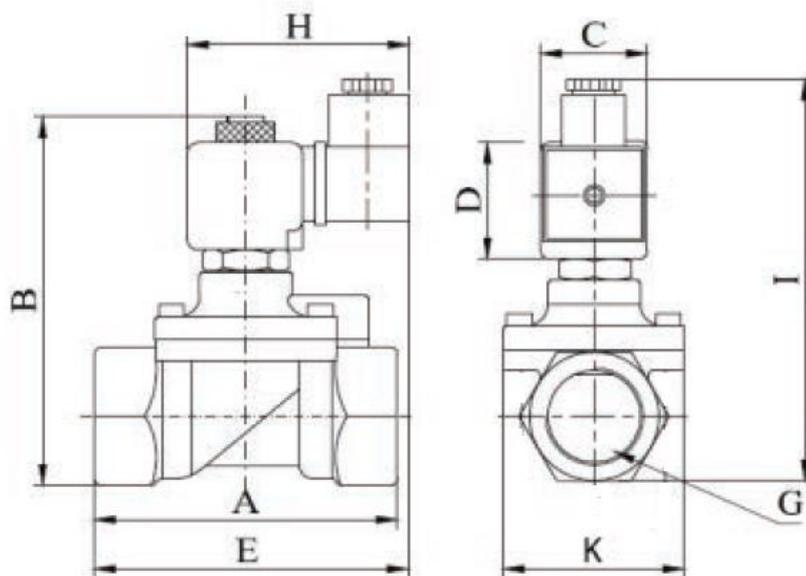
Габаритные и присоединительные размеры клапана типа EV250R
